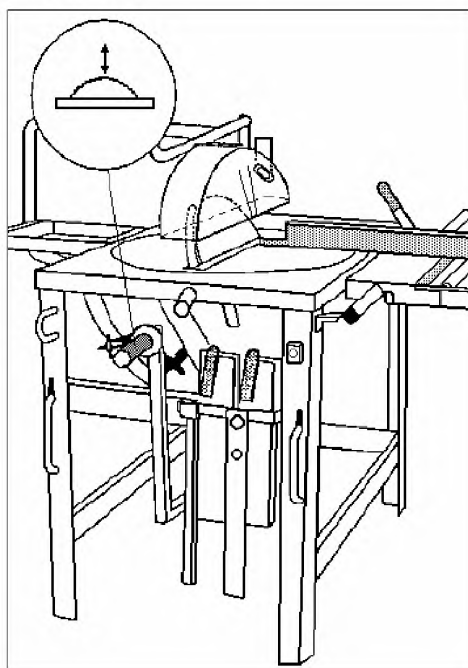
Пример для станка в режиме эксплуатации поперечного распиливания с неподвижно закрепленной заготовкой
